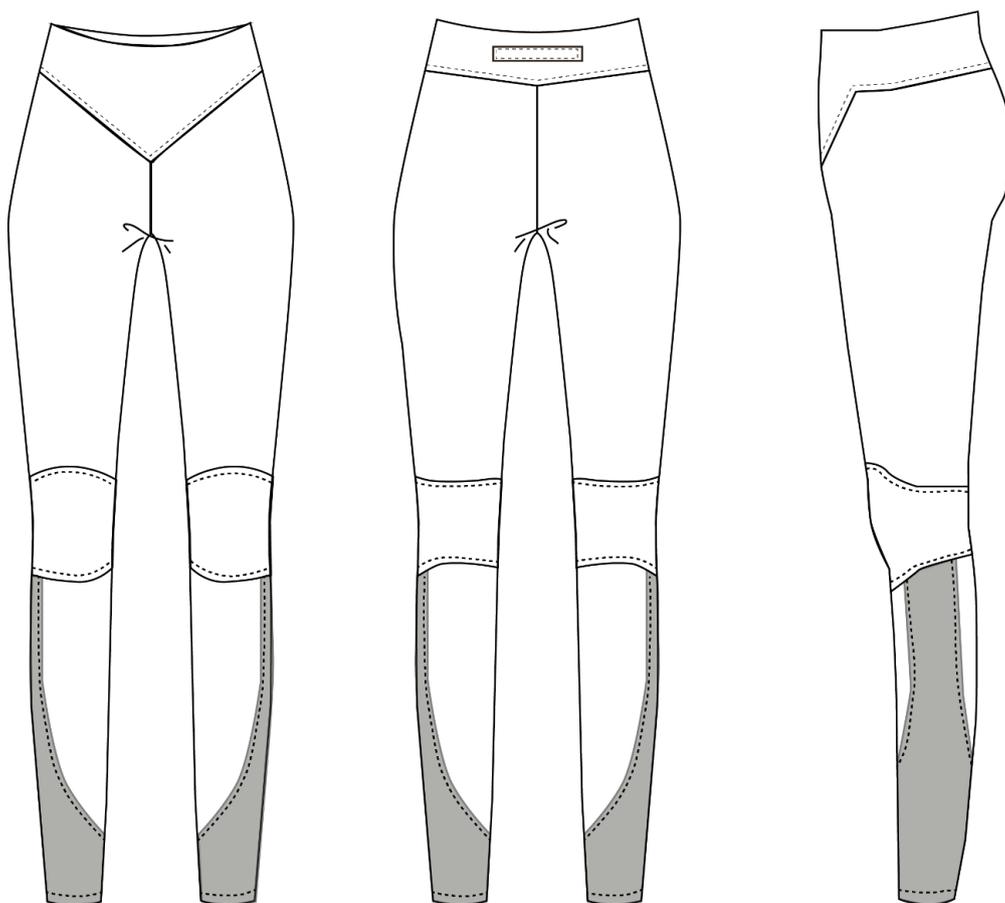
Desenho técnico do produto. (Fonte: Autora)
